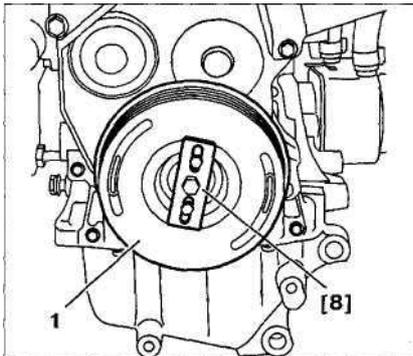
Снимите шкив 1 коленчатого вала с помощью приспособления [8].
